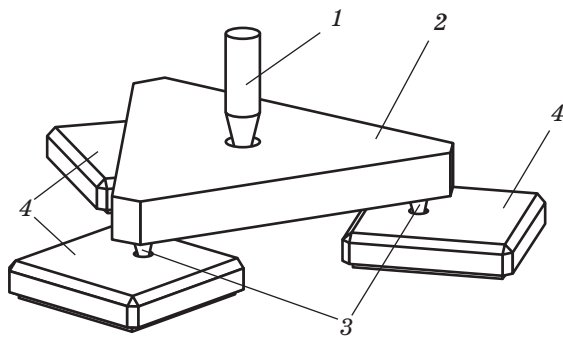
Фрагмент приспособления для обработки нескольких пластин одновременно. 1 – поводок, 2 – пластина, 3 – малые поводки, 4 – прижимы.
